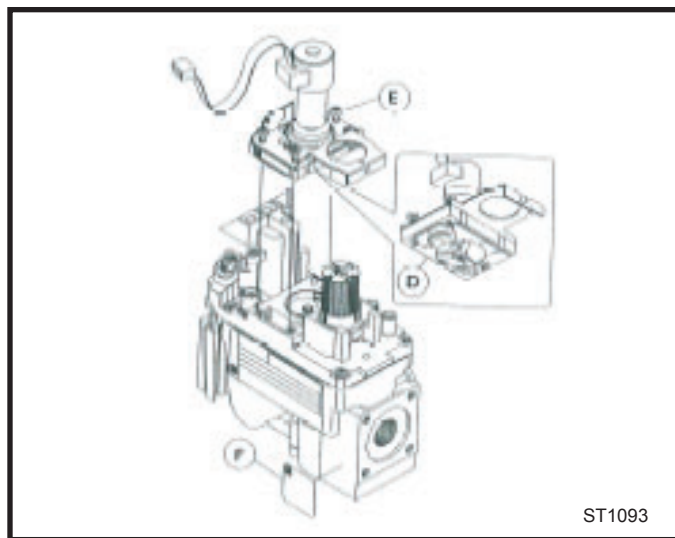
Retirez les vis de montage du régulateur. Remplacez le moteur pas à pas.
